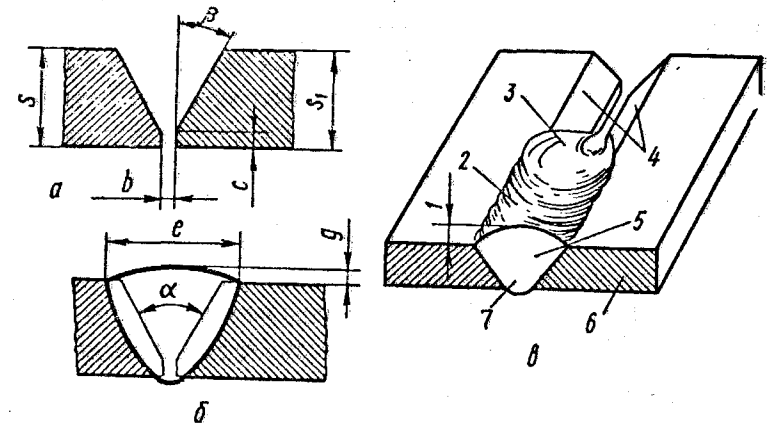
Стыковое сварное соединение: а — подготовка под сварку; б — выполненный шов; в — внешний вид соединения; 1 — усиление шва; 2 — сварной шов; 3 — сварочная ванна; 4 — кромки; 5 — металл шва; 6 — основной металл; 7 — корень шва
